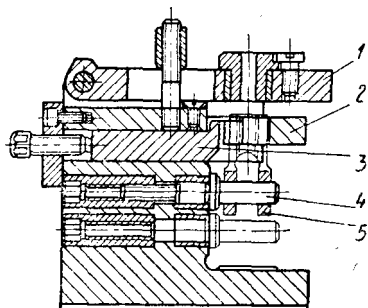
Наладочное приспособление для групповой обработки стяжек и вилок на вертикально-сверлильных станках
